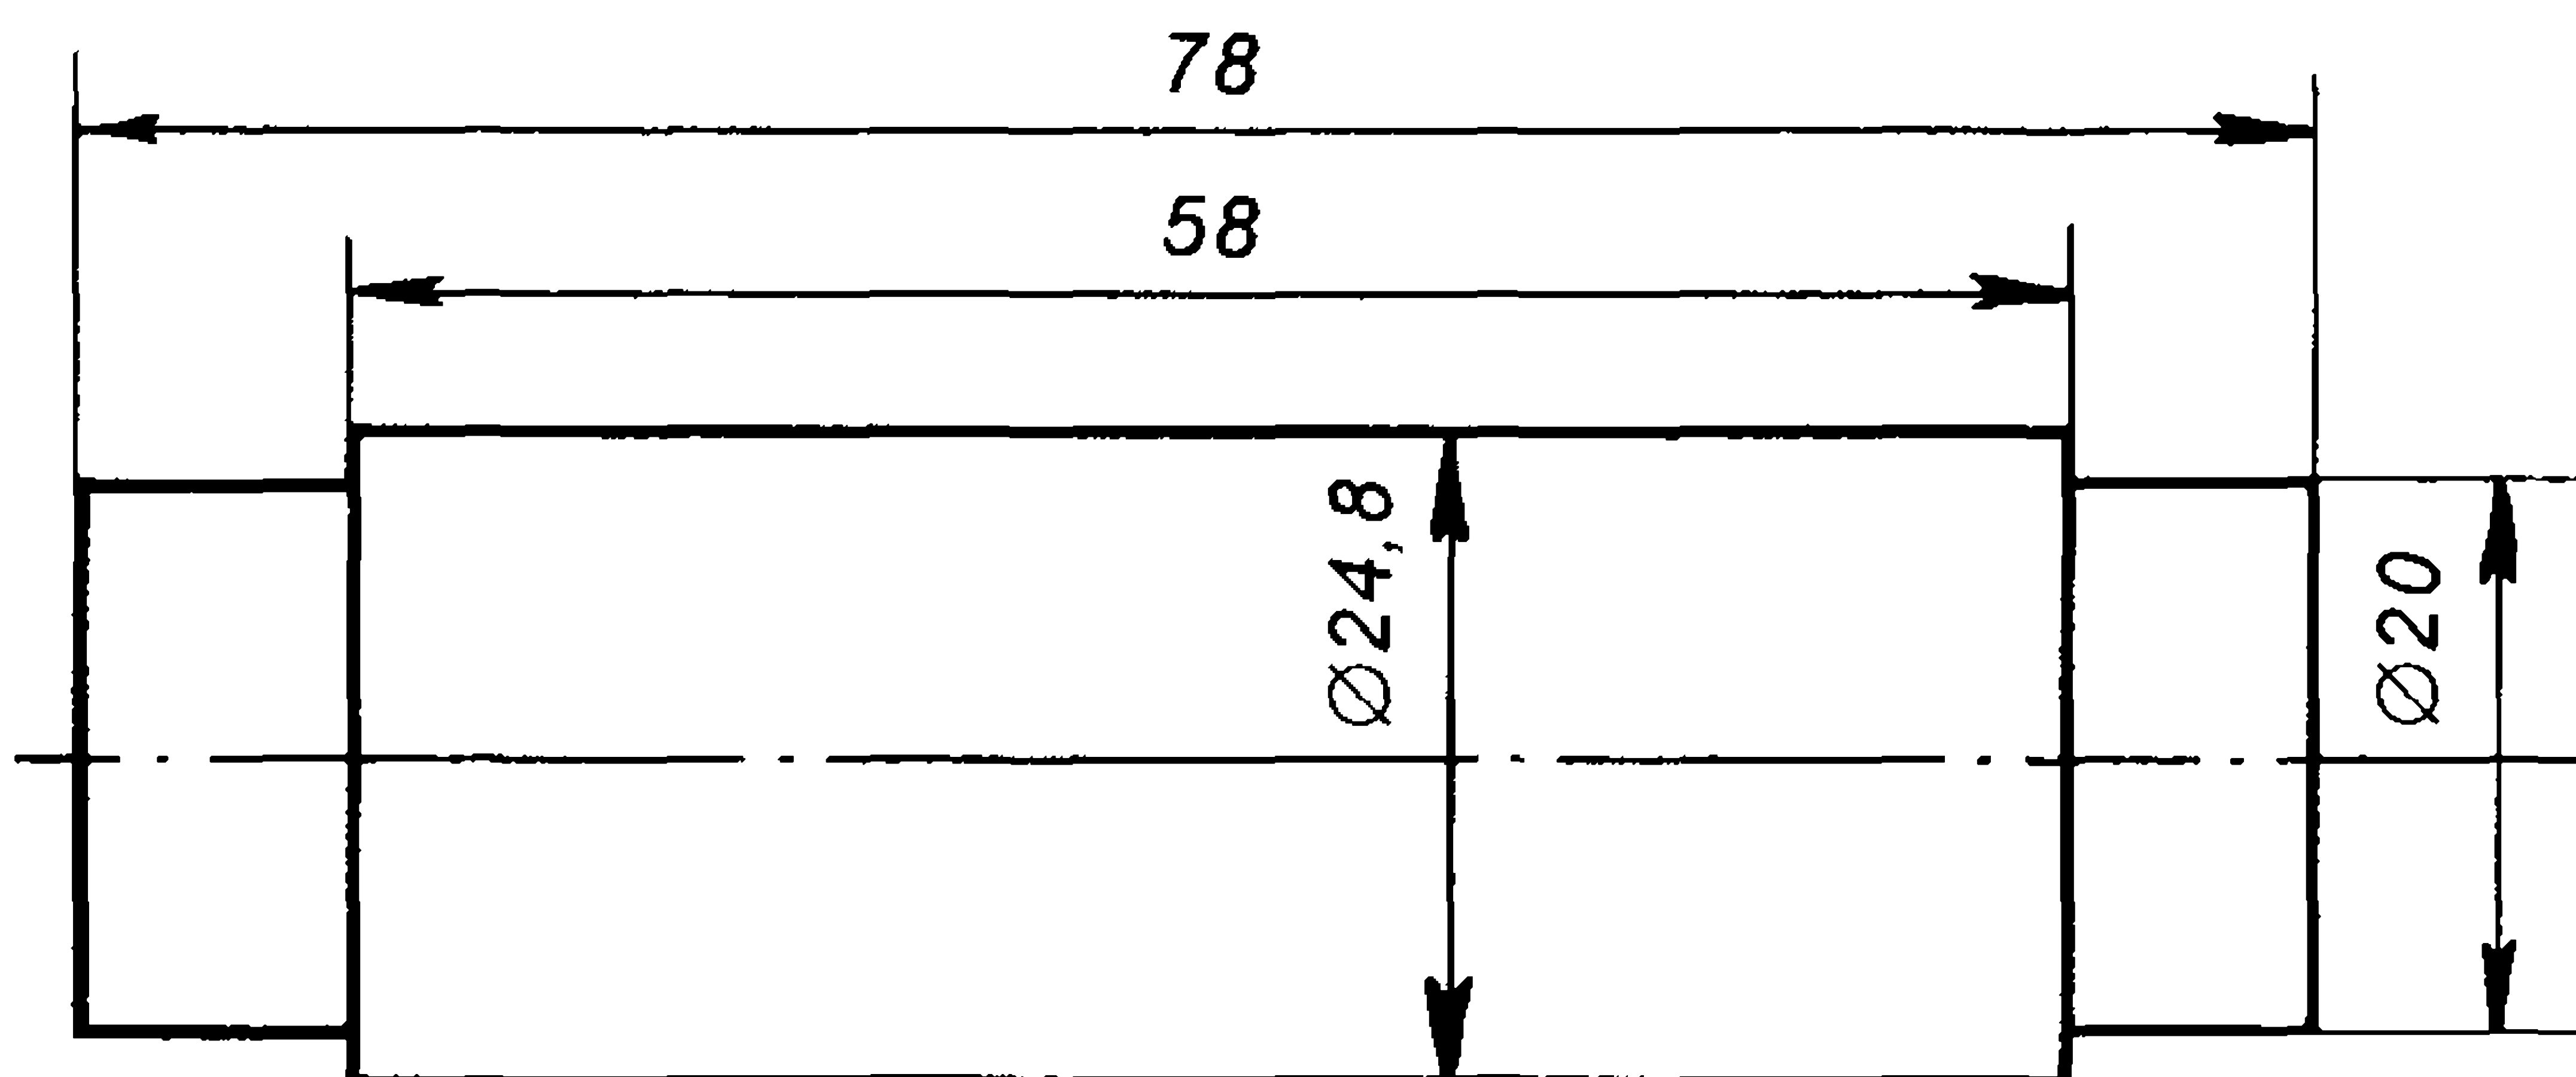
Оправка для запрессовки поршневого пальца в поршень и шатун
